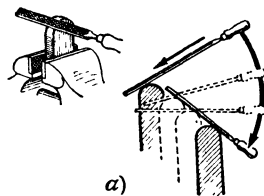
Крепление тисков к столу, рабочая „стойка“ при работе напильником и опилование вперекрестку.
